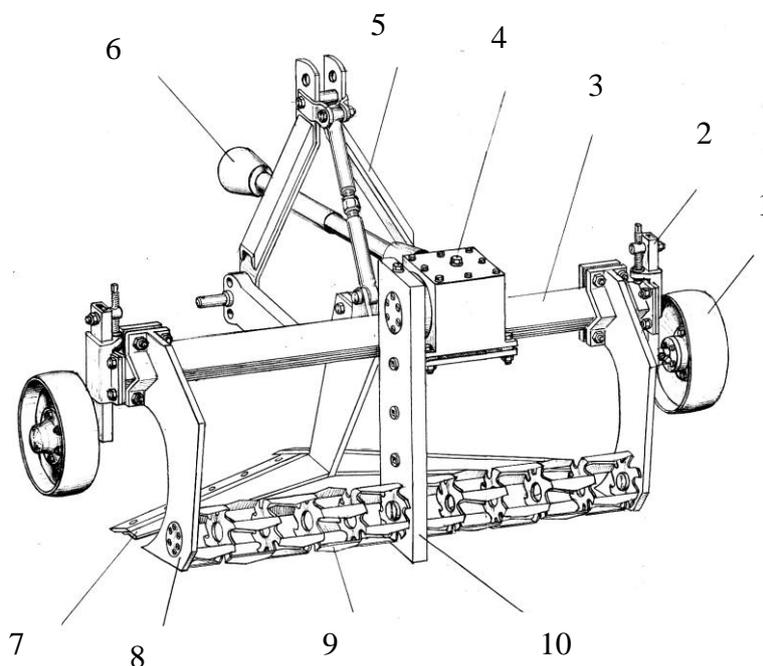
Схема комбинированного подпокрывного фрезерователя:
